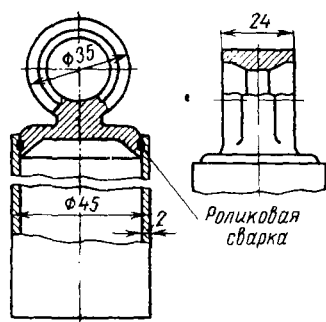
Цилиндр гидроамортизатора автомобиля
